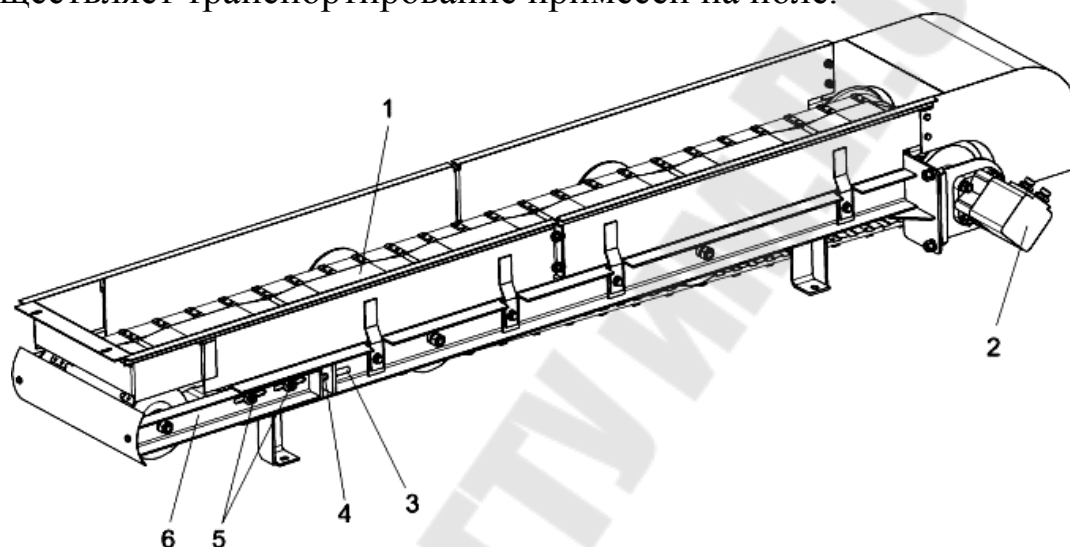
Транспортер примесей: 1 – лента транспортера; 2 – гидромотор; 3, 5 – болты фиксирующие; 4 – контргайка; 6 – механизм натяжной
